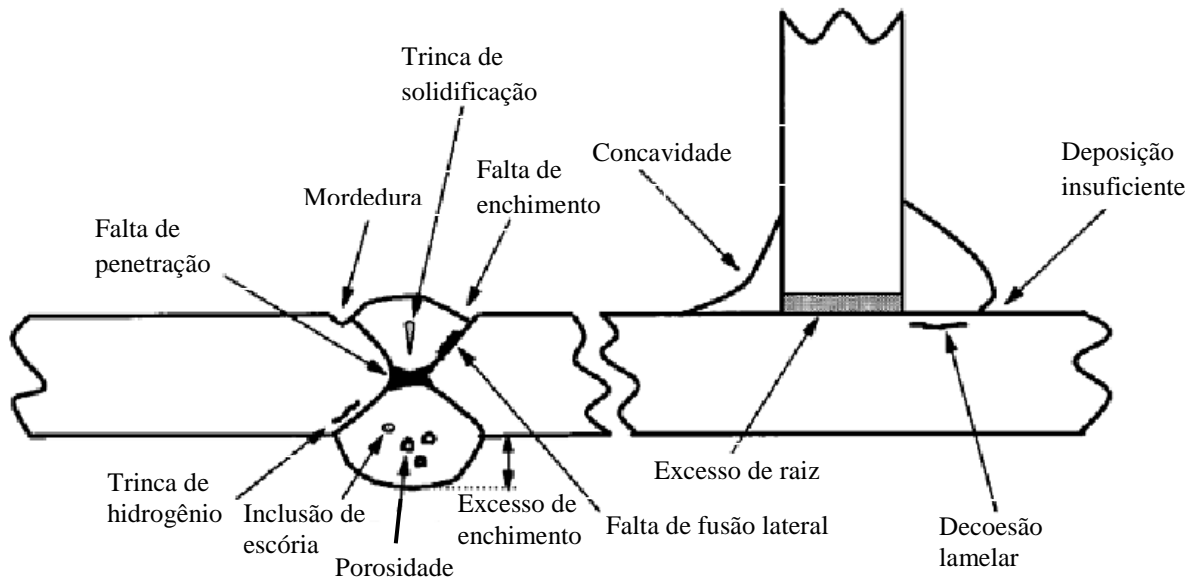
Defeitos encontrados em juntas soldadas
